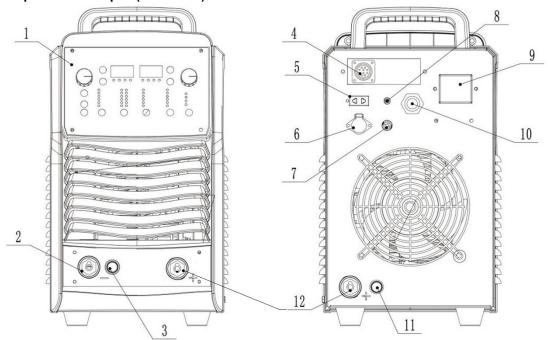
Общий вид сварочного аппарата (источника) спереди/сзади
